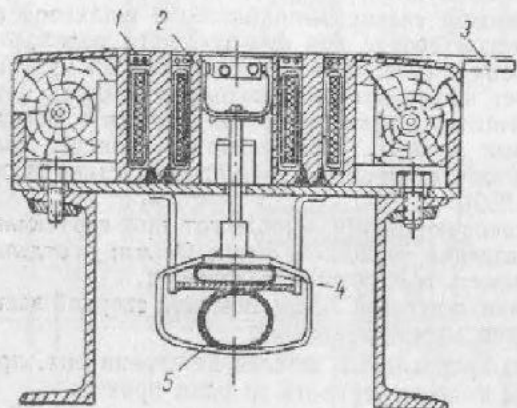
Флюсовая подушка для автоматической сварки.
